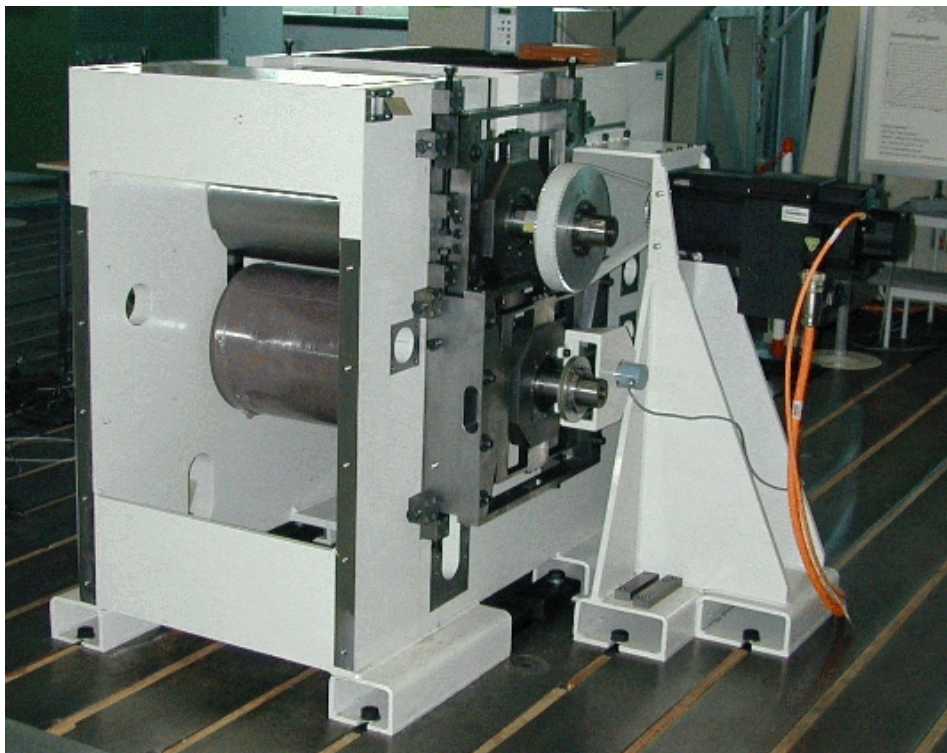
Versuchsstand im Versuchsfeld des Fraunhofer Instituts Werkzeugmaschinen und Umformtechnik in Chemnitz
